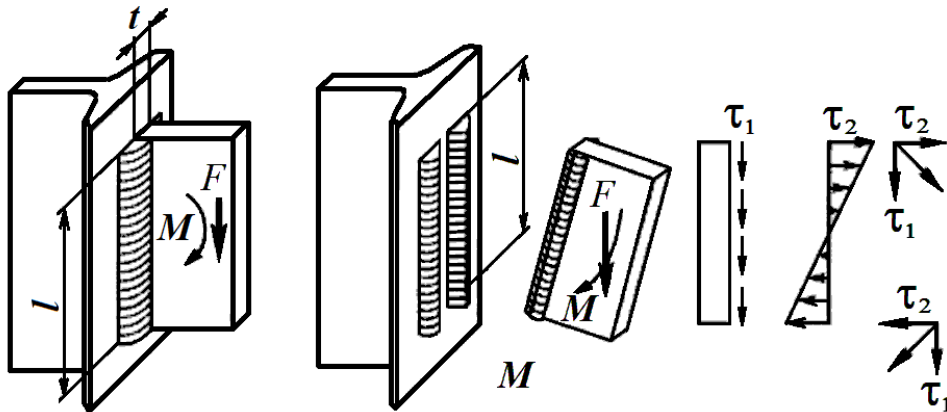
Схема нагружения угловых сварных швов таврового соединения силой F и моментом M
